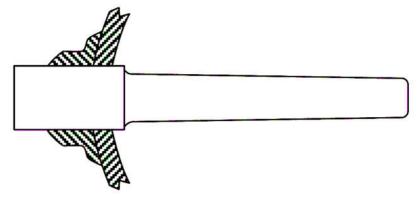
Пример установки гильзы под приварку через адаптер (Socket Weld).
